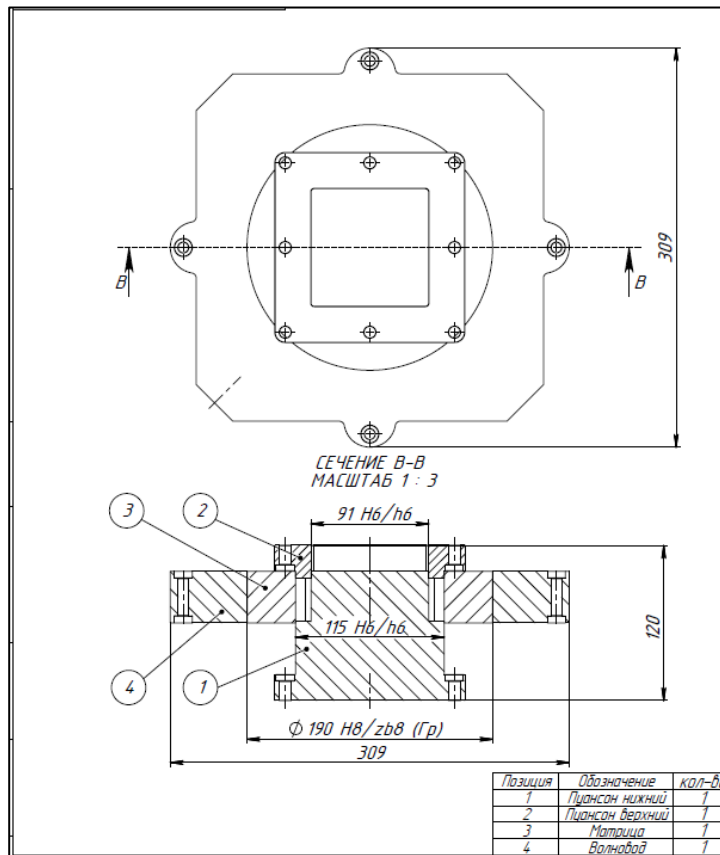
Фрагмент сборочного чертежа ЭКД пресс-формы
